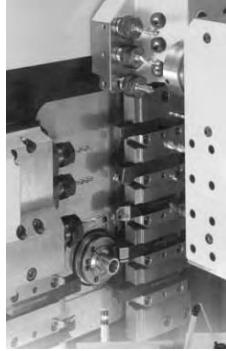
Поперечні супорти токарного багатоцільового верстата
